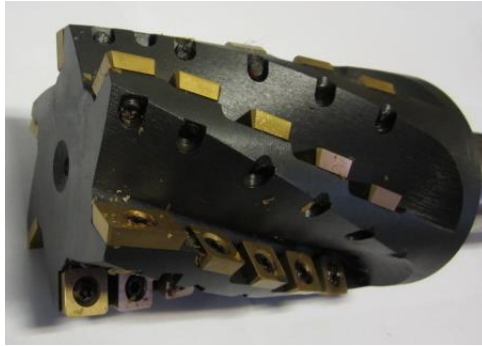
Кінцева фреза з багатограними пластинками
